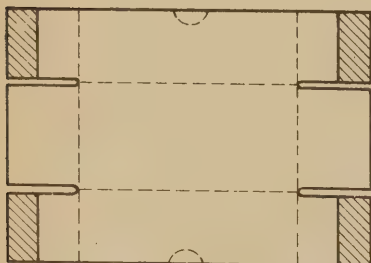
Zuschnitt für Schachteln mit Drahtheftung und Einschlageecken.
